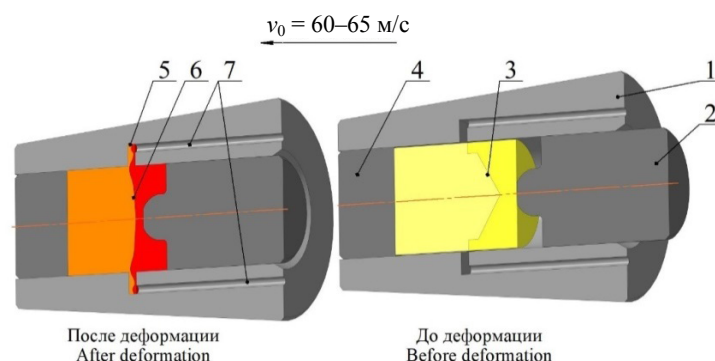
Схема деформирования для скоростного горячего выдавливания биметаллических полуфабрикатов детали «вставка пуансона»: 1 – полуматрица; 2 – формообразующий пуансон; 3 – составная заготовка; 4 – подпор; 5 – кольцевая проточка; 6 – биметаллический полуфабрикат; 7 – газоотводящие каналы
